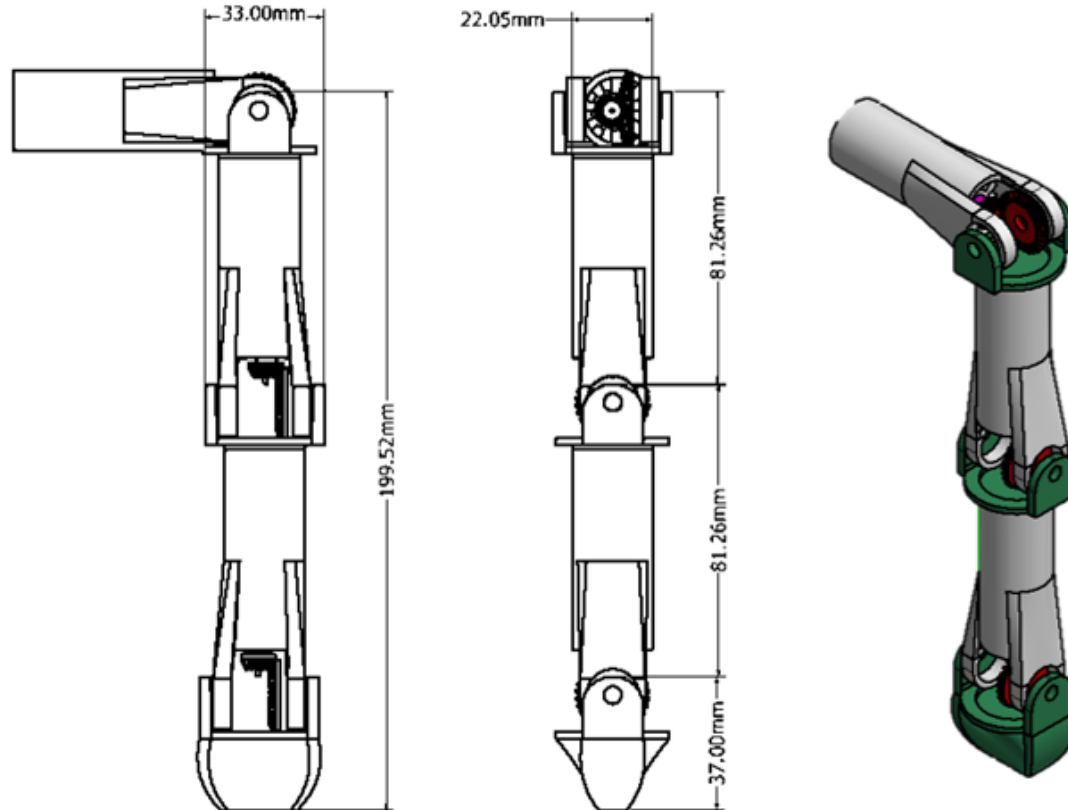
Diseño y dimensiones de brazo con motores Hitec (Diseño 1)
